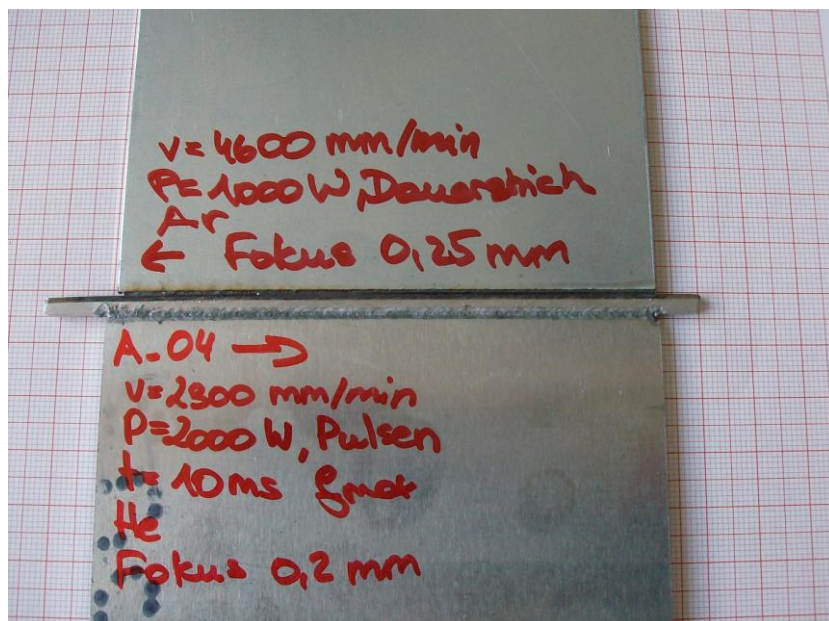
Sekundärschweißung ohne Zusatz, Vorderseite; oben Stahlschweißung, unten Aluminiumschweißung
